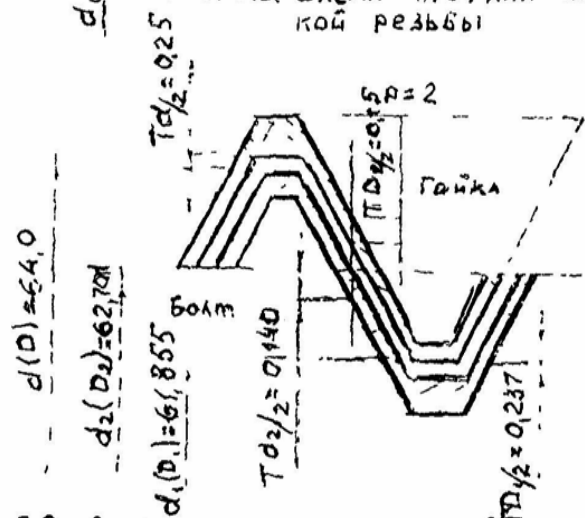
Схема расположения полей допусков резьбы
